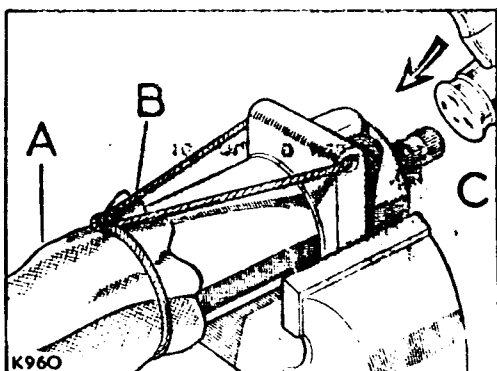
Desmontaje del eje de la caja compensadora.
